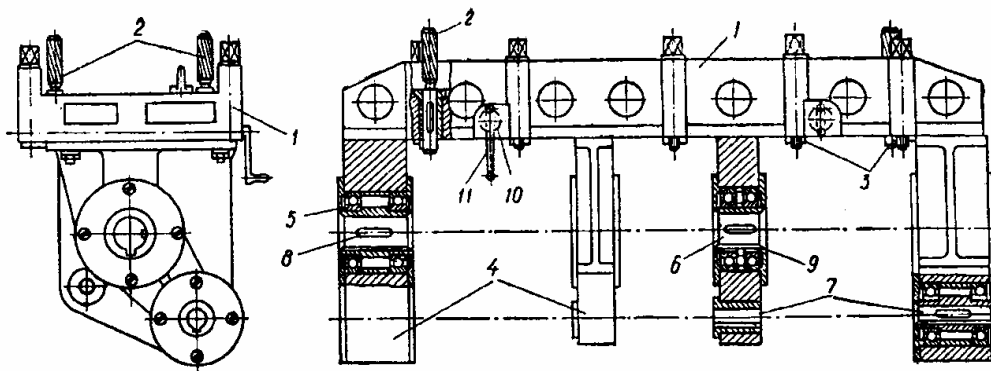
Пристрій (кондуктор) для розточування гнізд корінних підшипників блока циліндрів: 1 – корпус; 2 – установочні штифти; 3 – пластини; 4 – опорні кронштейни; 5 і 7 – підшипники; 6 – напрямні втулки; 8 – шпонки; 9 – пази; 10– ексцентрики; 11 – рукоятка
